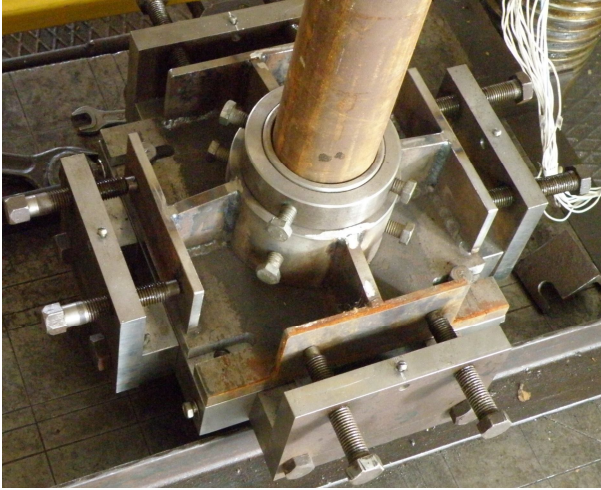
Общий вид опорного приспособления (нижняя опора)
